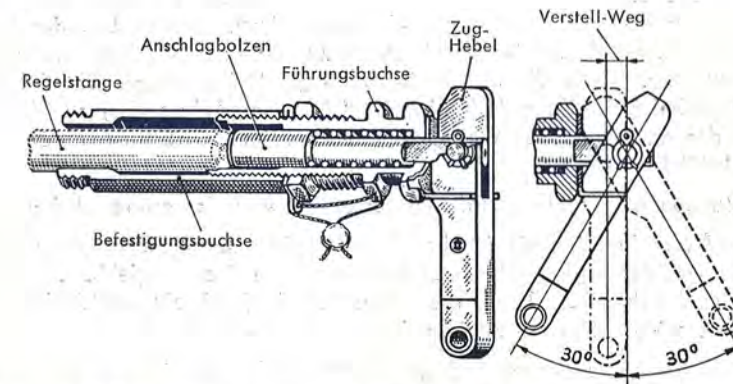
Regelstangen-Anschlag mit Zughebel für Mehrmenge beim Anlassen
